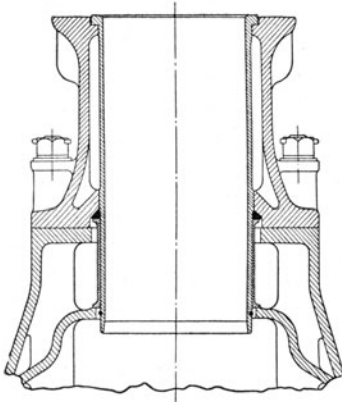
Zylinderbauart mit lose eingesetzter, durch Gummiring abgedichteter und im Einsatz gehärteter Stahllaufbüchse.
